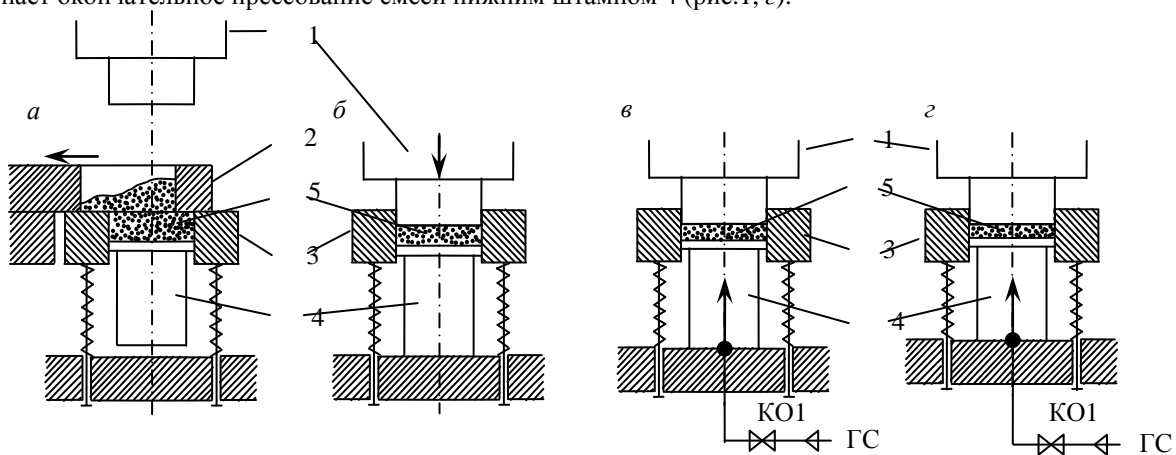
Схема процесса прессования порошкообразной смеси на базе гидропресса:
